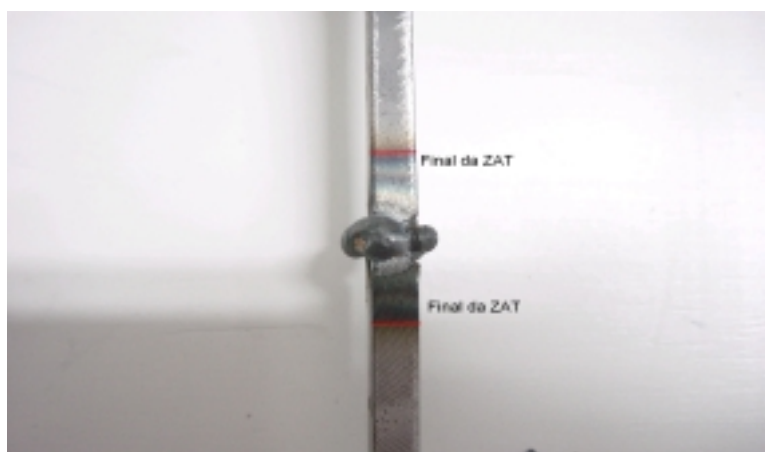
Área da ZAT Corpo de Prova Soldagem Robotizada
